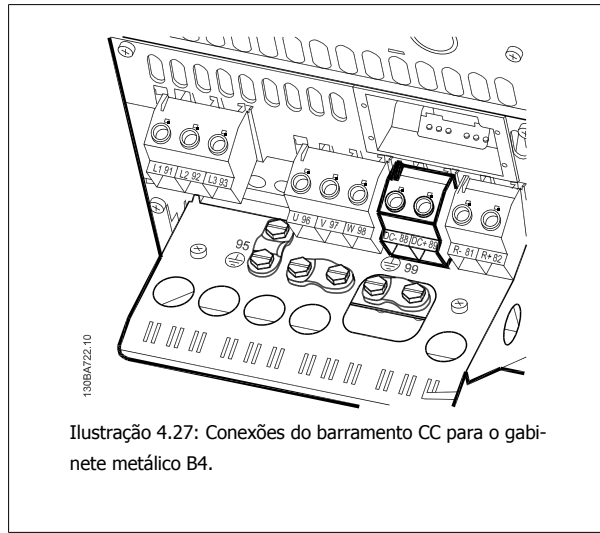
Conexões do barramento CC para o gabinete metálico B4.
